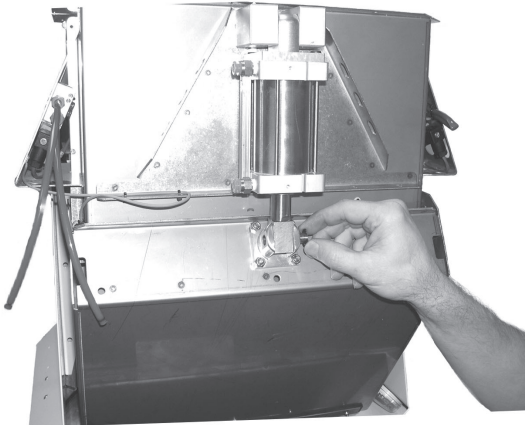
Entfernen des Schwenkhebelbolzens
